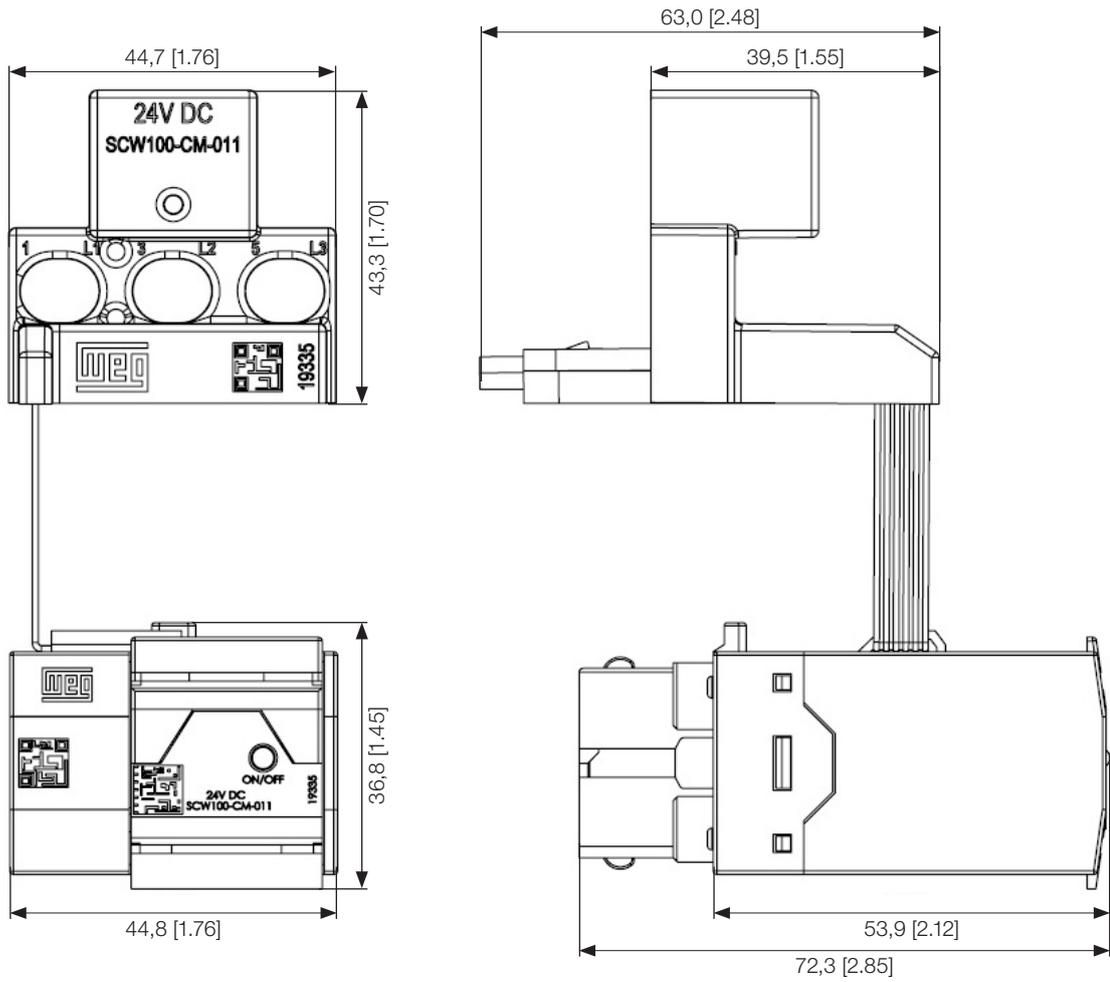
Dimensiones del Módulo de Conexión Arranque Directo con guardamotor (CM-011) en mm [in]
